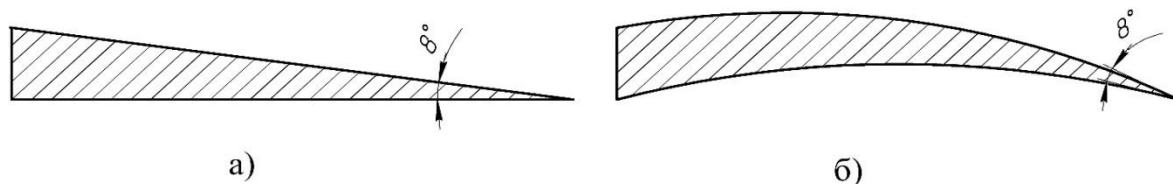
Профили сечений лопасти СКВ: а – с прямой поверхностью; б – с искривленной поверхностью
